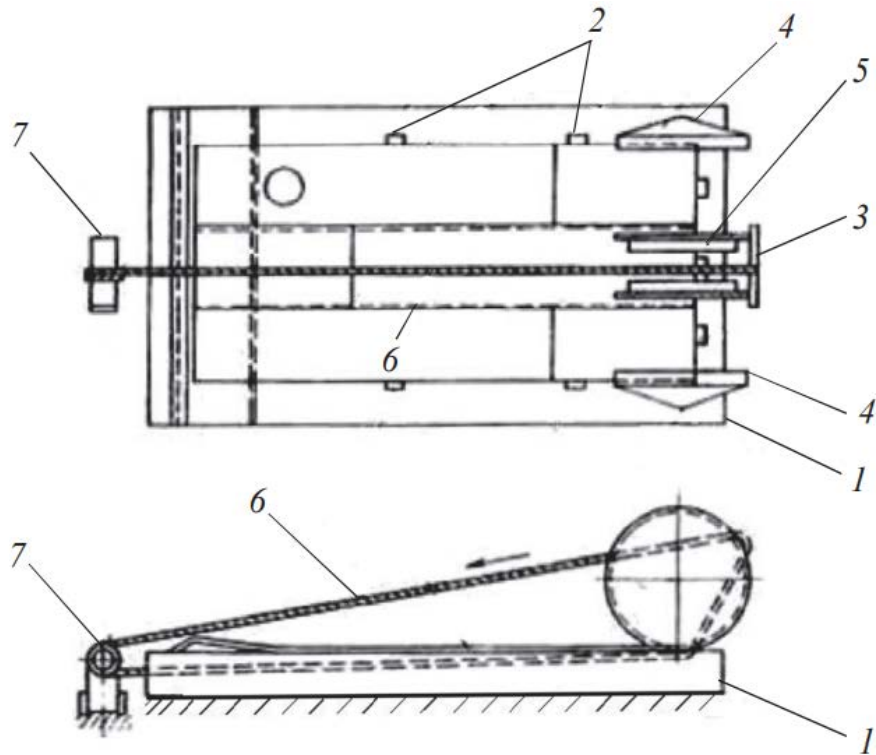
Складальний стенд; 2 - нерухомі упори; 3 - допоміжна балка; 4 - днища; 5 - ребра жорсткості; 6 - канат; 7 - електролебідка
